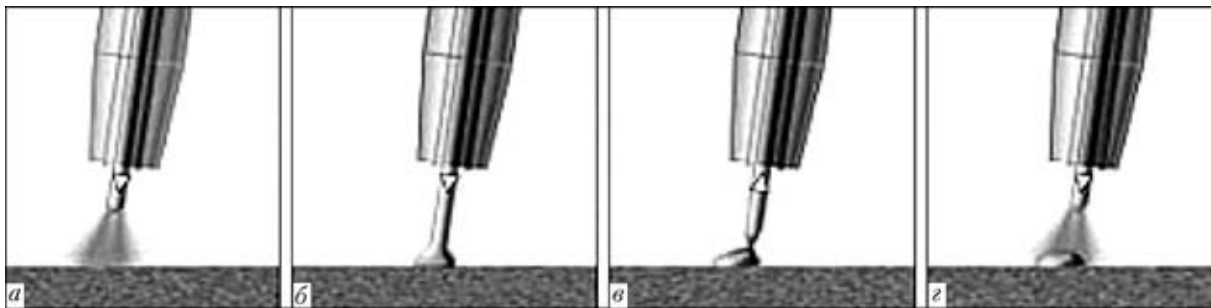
Цикл переноса электродного металла при СМТ сварке: а, б, с — движение проволоки в зону горения дуги; в — реверсивное движение
